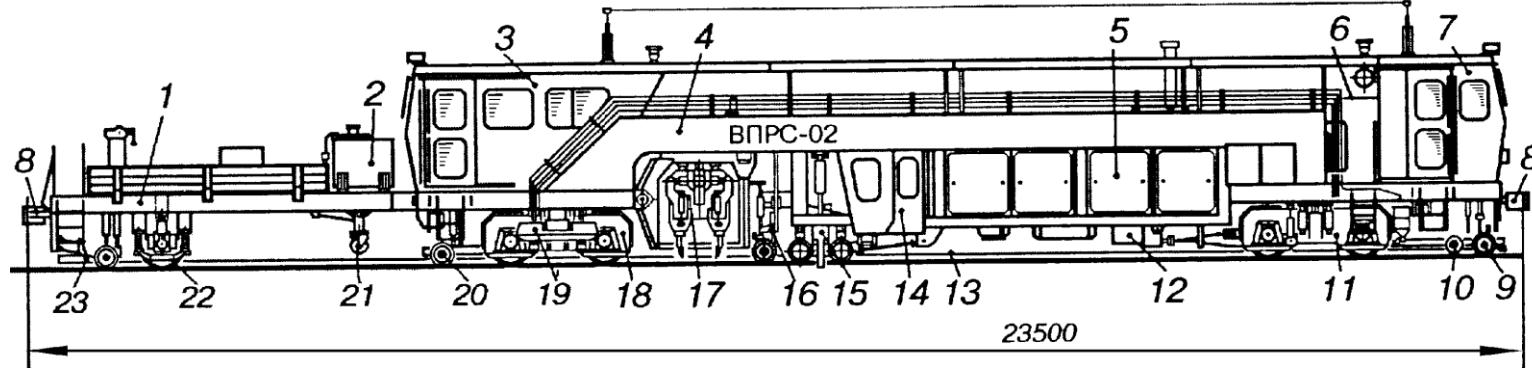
Выправочно-подбивочно-рихтовочная машина для стрелок и пути ВПРС-02: 1 – полуприцепная платформа; 2 – дополнительный топливный бак; 3, 7, 14 – кабины машиниста, оператора и рабочая; 4 – рама; 5 – дизельная силовая установка; 6 – тросы нивелировочно-измерительной системы; 8 – автосцепки; 9, 20, 23 – передняя, контрольно-измерительная и задняя тележки КИС; 10 – мерный каток с датчиком пройденного пути; 11, 18 – тяговая и бегунковая тележки; 12 – силовая передача (трансмиссия); 13 – трос-хорда рихтовочной КИС; 15 – ПРУ; 16 – нивелировочно-рихтовочное измерительное устройство КИС; 17 – одношпальные подбивочные блоки; 19 – уплотнители балласта у торцов шпал; 21 – опора платформы; 22 – колёсная пара
